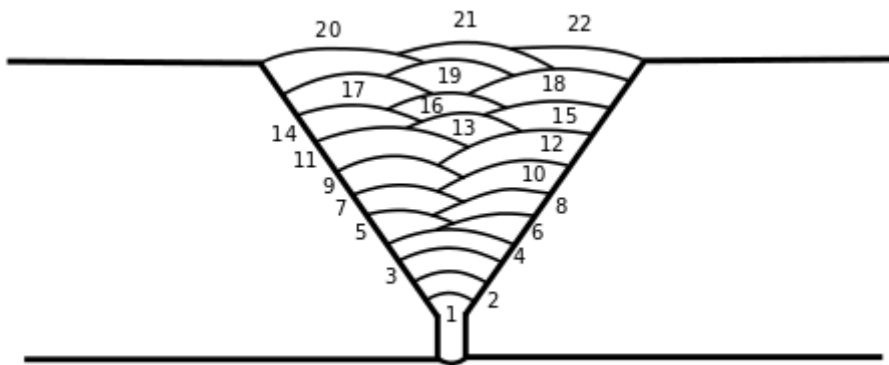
Corpo de prova 2 com restrição – Diagrama dos passe de soldagem GTAW
